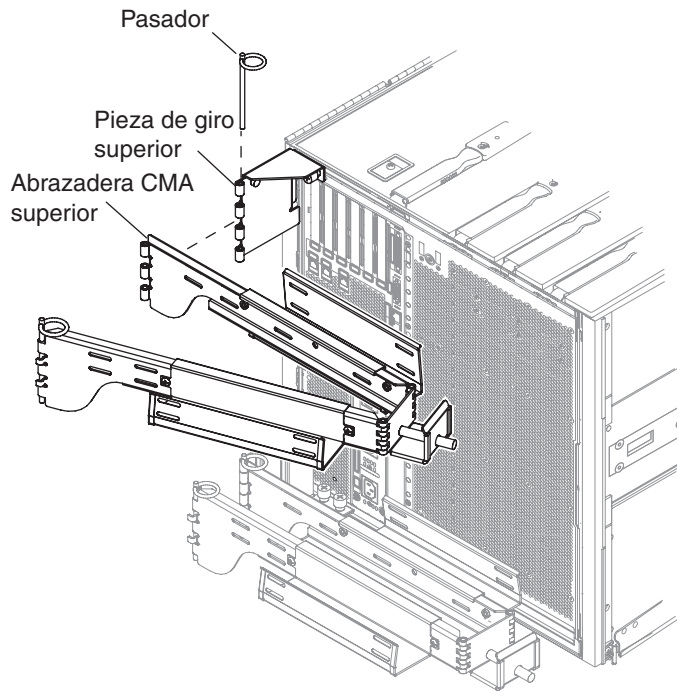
Montaje de la abrazadera CMA superior y la pieza de giro
